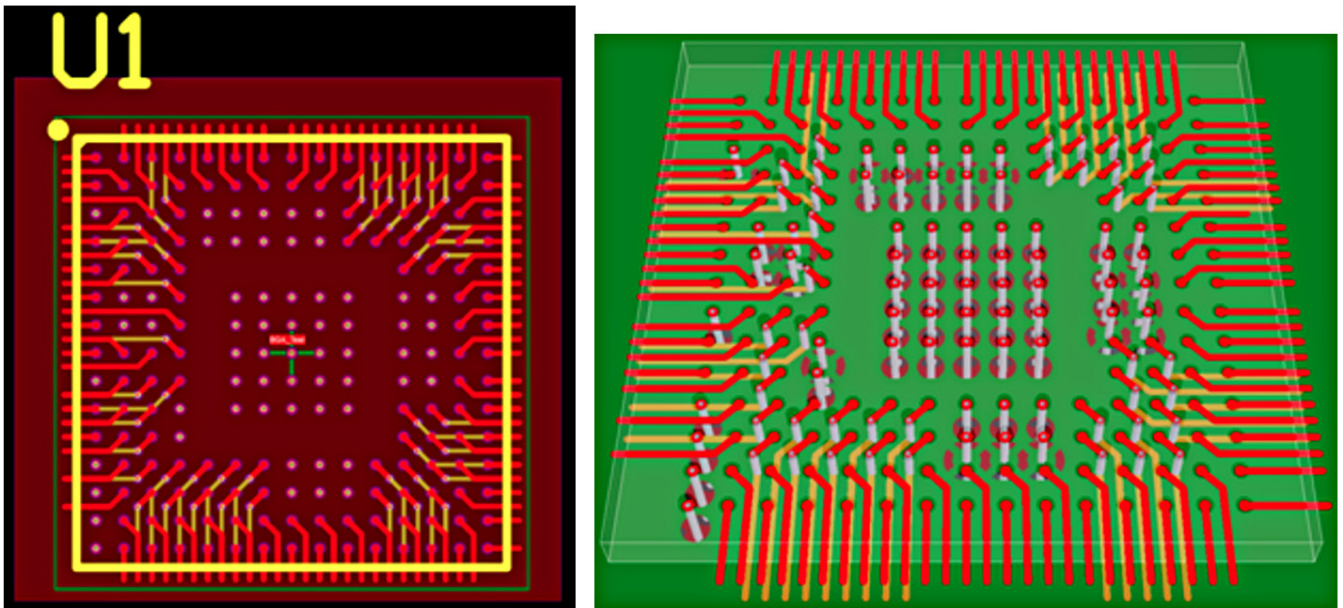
Cavo di segnale con fanout ed escape routing e collegamento all'alimentazione in modalità "via-in-pad".
